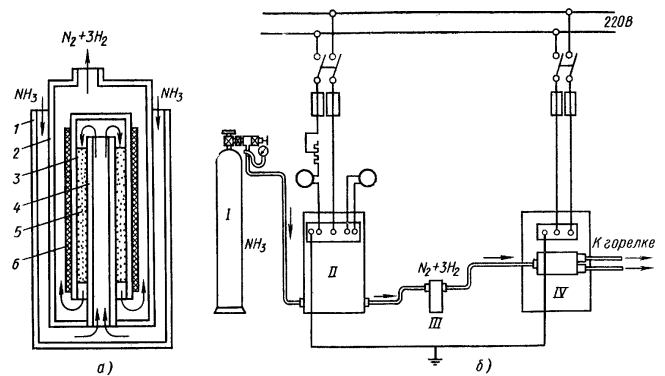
Схемы крекера (а) и установки (б) для сварки азотно-водородной смесью:
